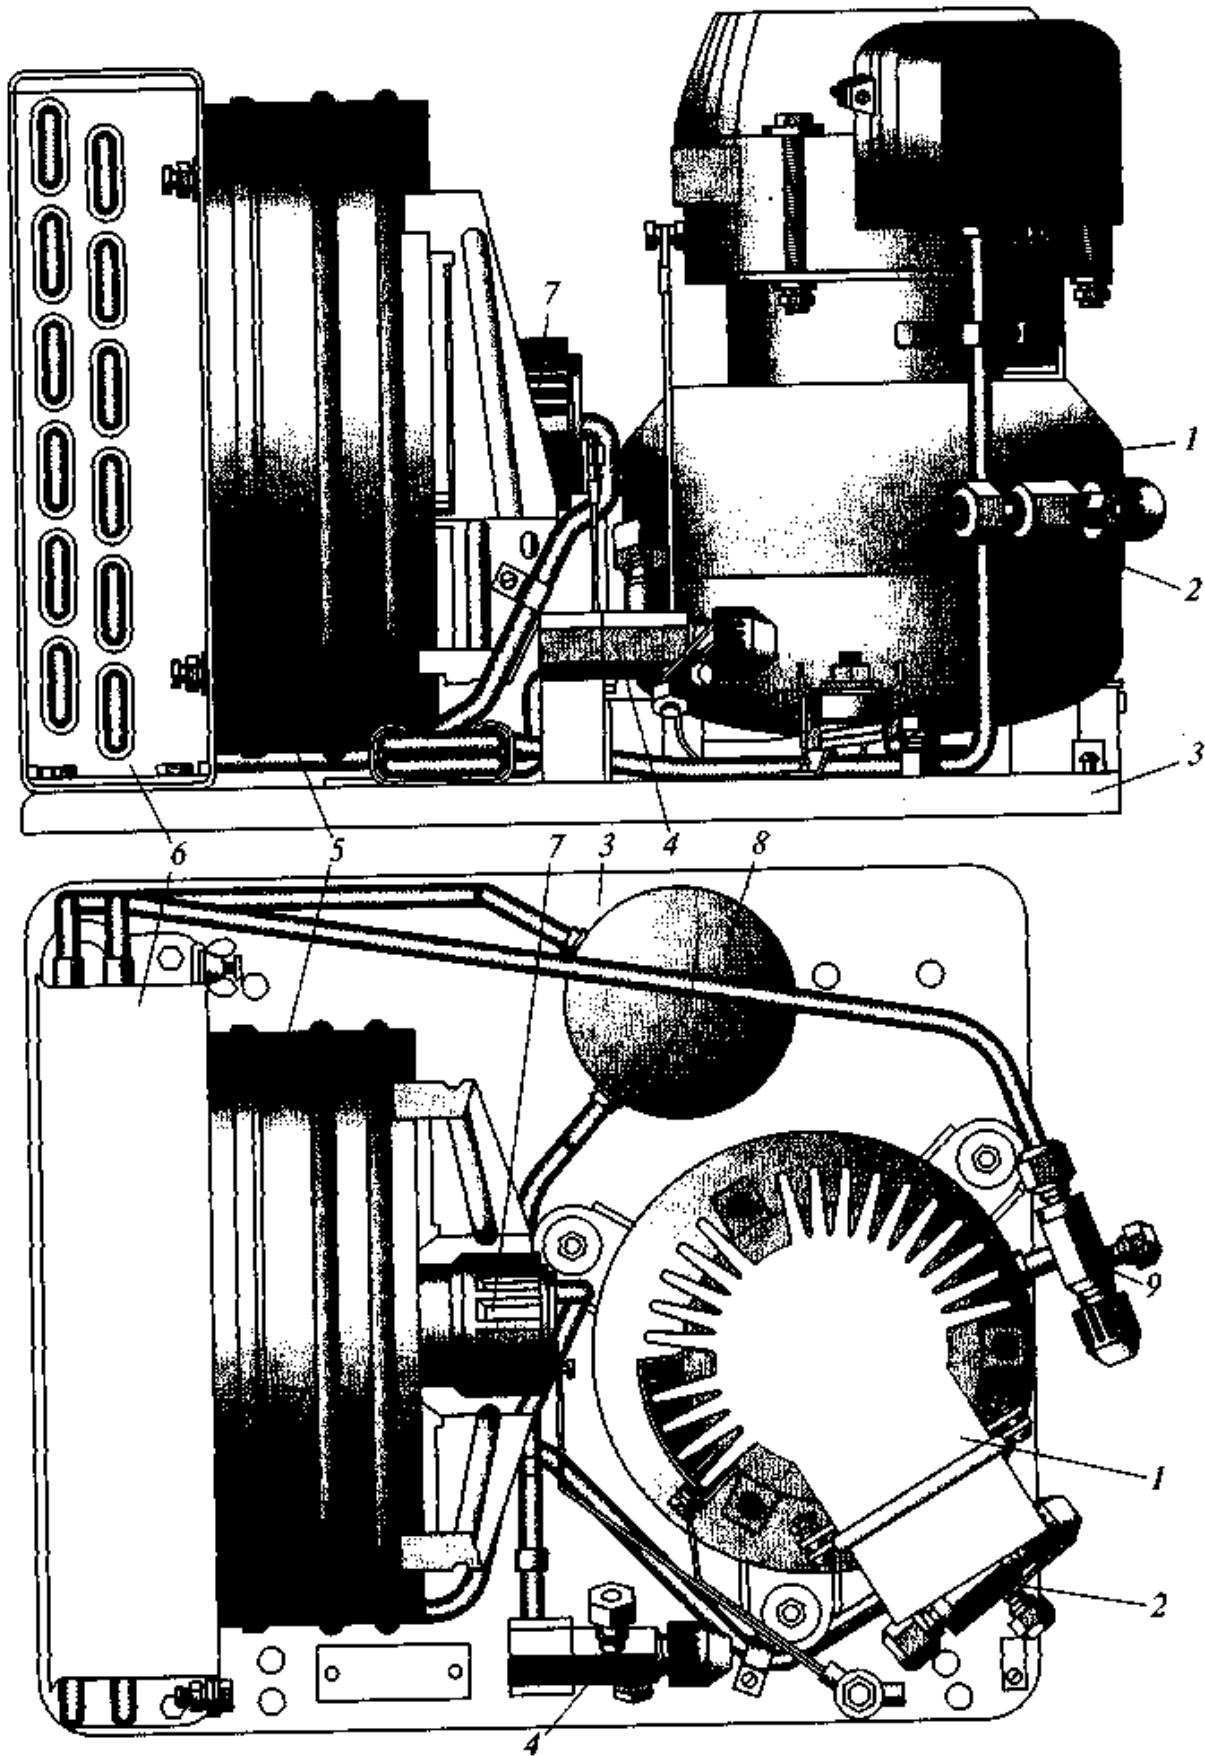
Компрессорно-конденсаторный агрегат с герметичным компрессором и экранированным двигателем (типа ВСэ):
